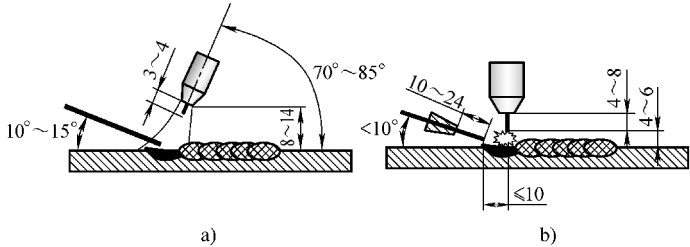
氩弧平焊时的焊枪焊丝位置
